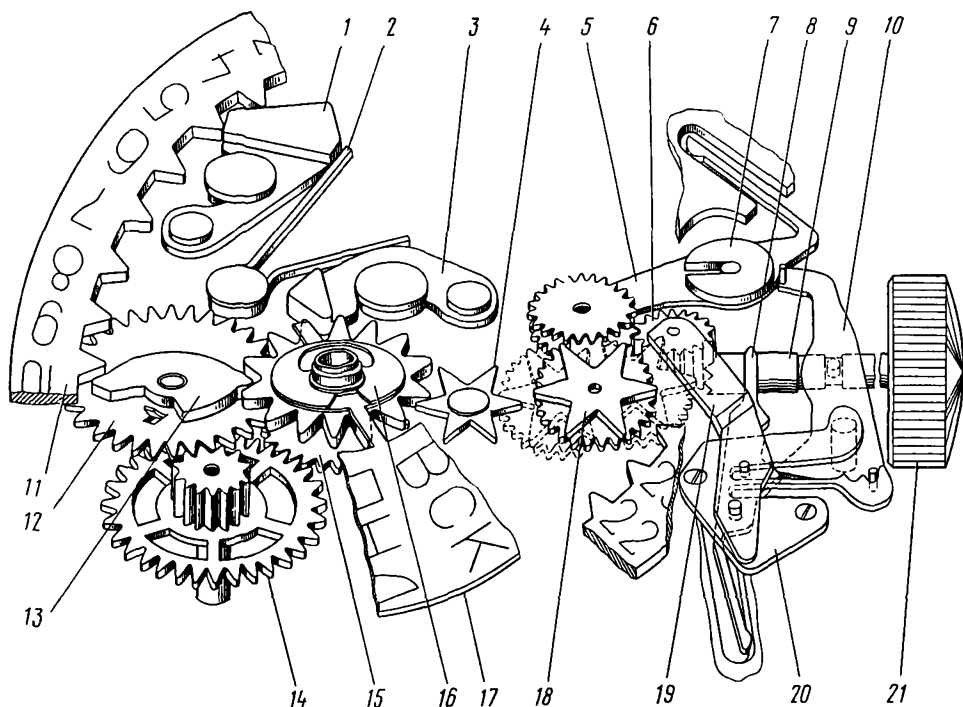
Кинематическая схема календарного устройства механизма часов 2450:
